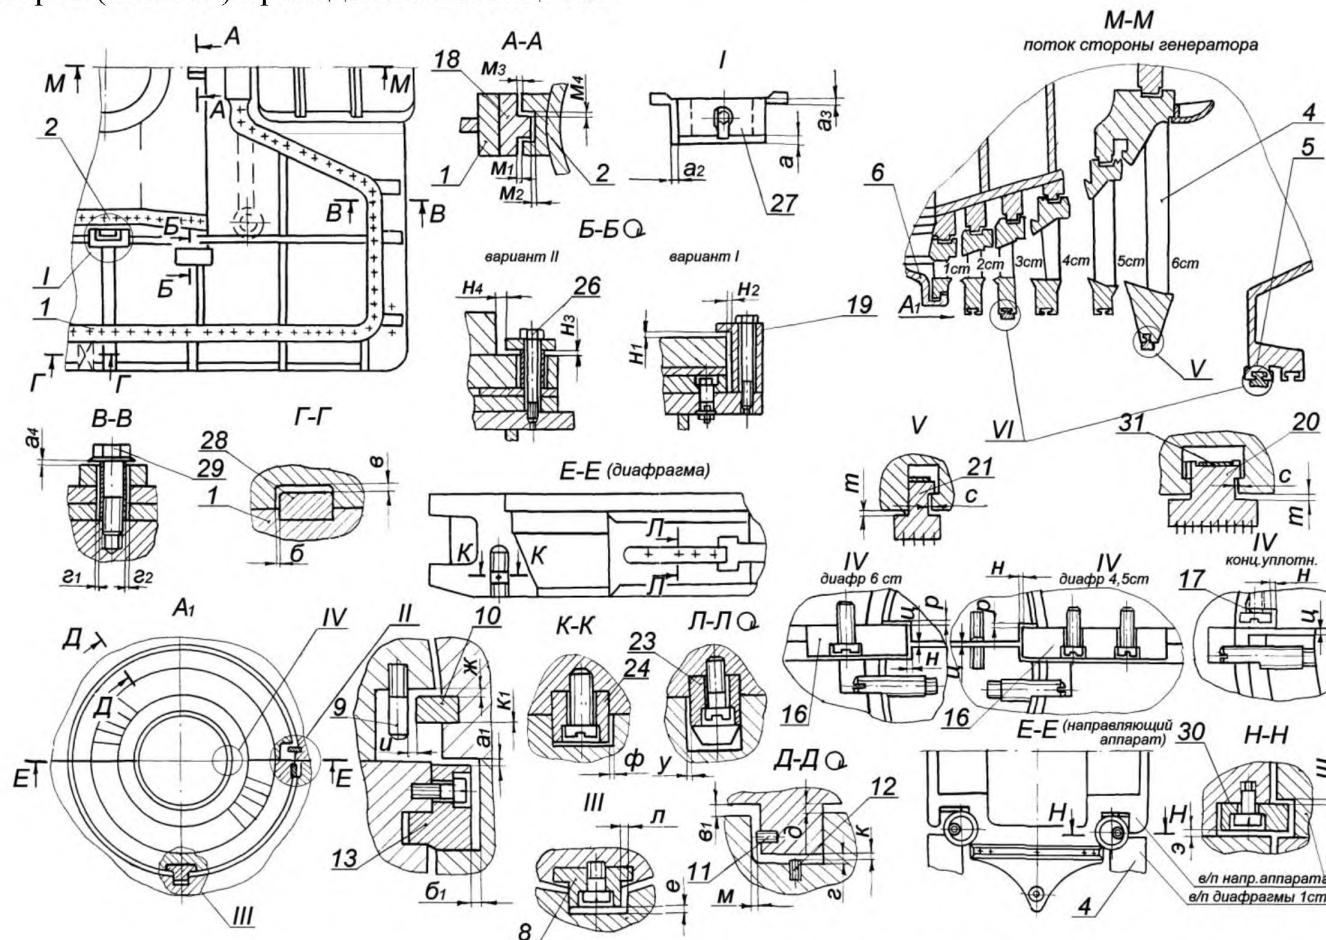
, лист 2 – Корпусные части цилиндра ВД
